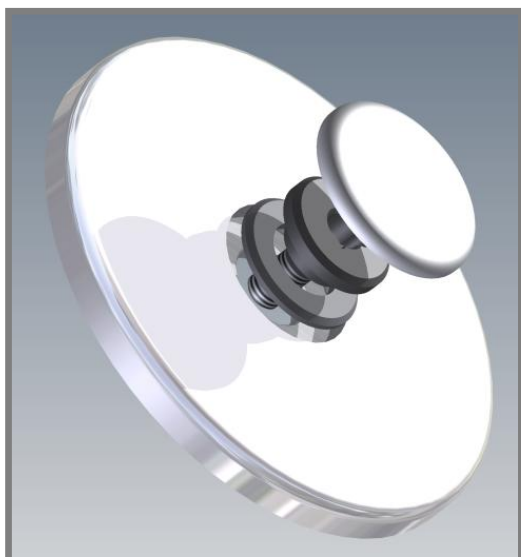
Obrázek otočného kroužku a ochranného krytu
